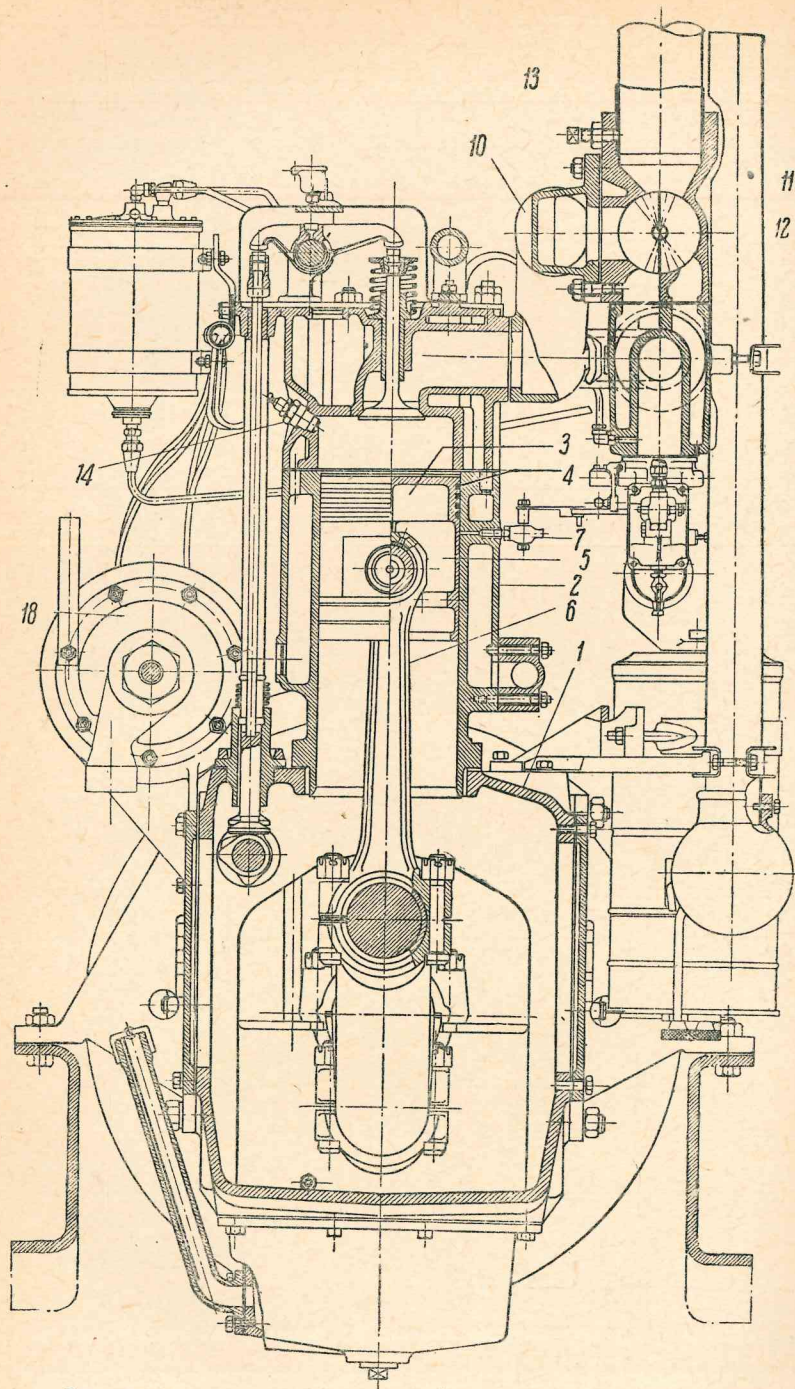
Поперечный разрез двигателя „Сталинец-60“ ЧТЗ
